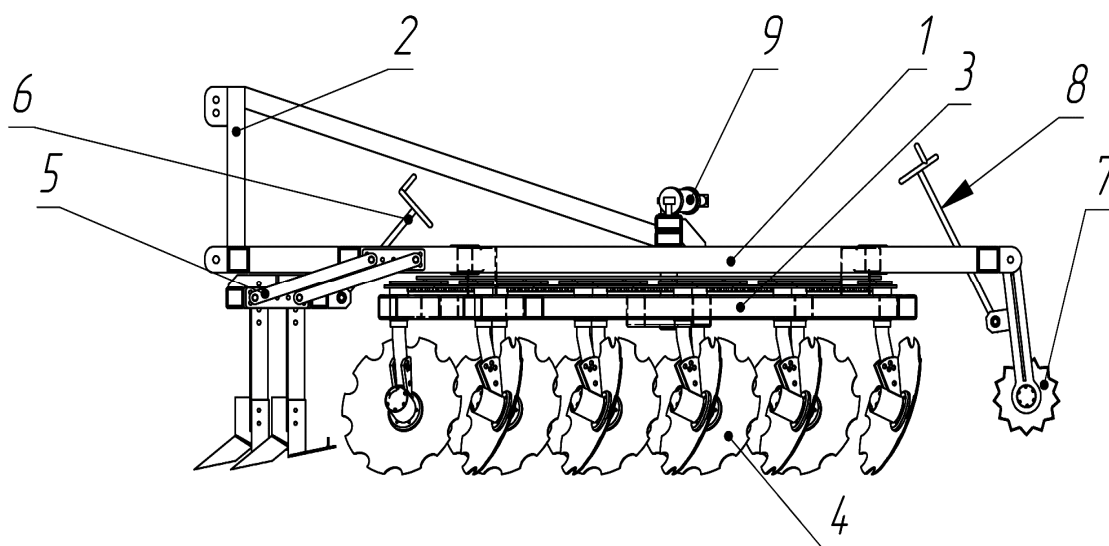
Универсальный плуг с поворотной балкой (вид сбоку)
